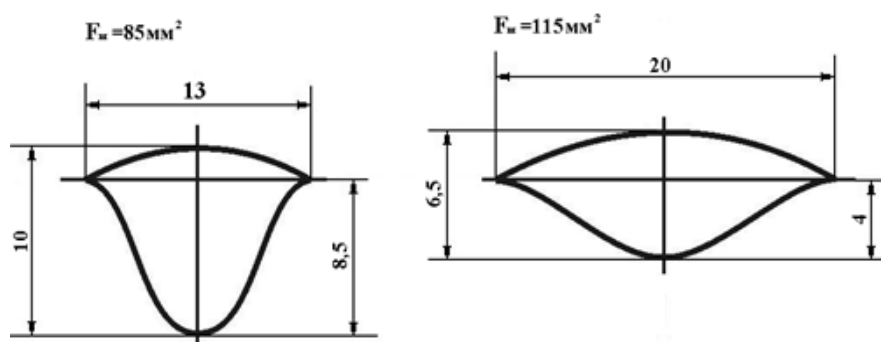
Изменение геометрических параметров сварного валика при автоматической сварке в защитной среде аргона [4]: а – ИП обычным способом; б – ИП с комплексным воздействием на жидкий металл сварочной ванны
